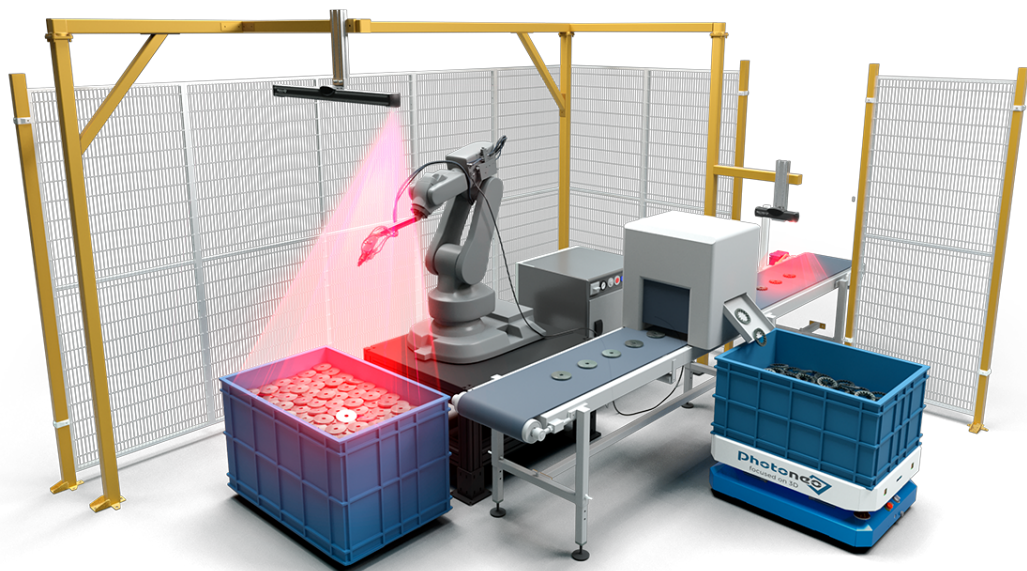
Získanie 3D obrazu metódou priestorového zobrazovania [6].
